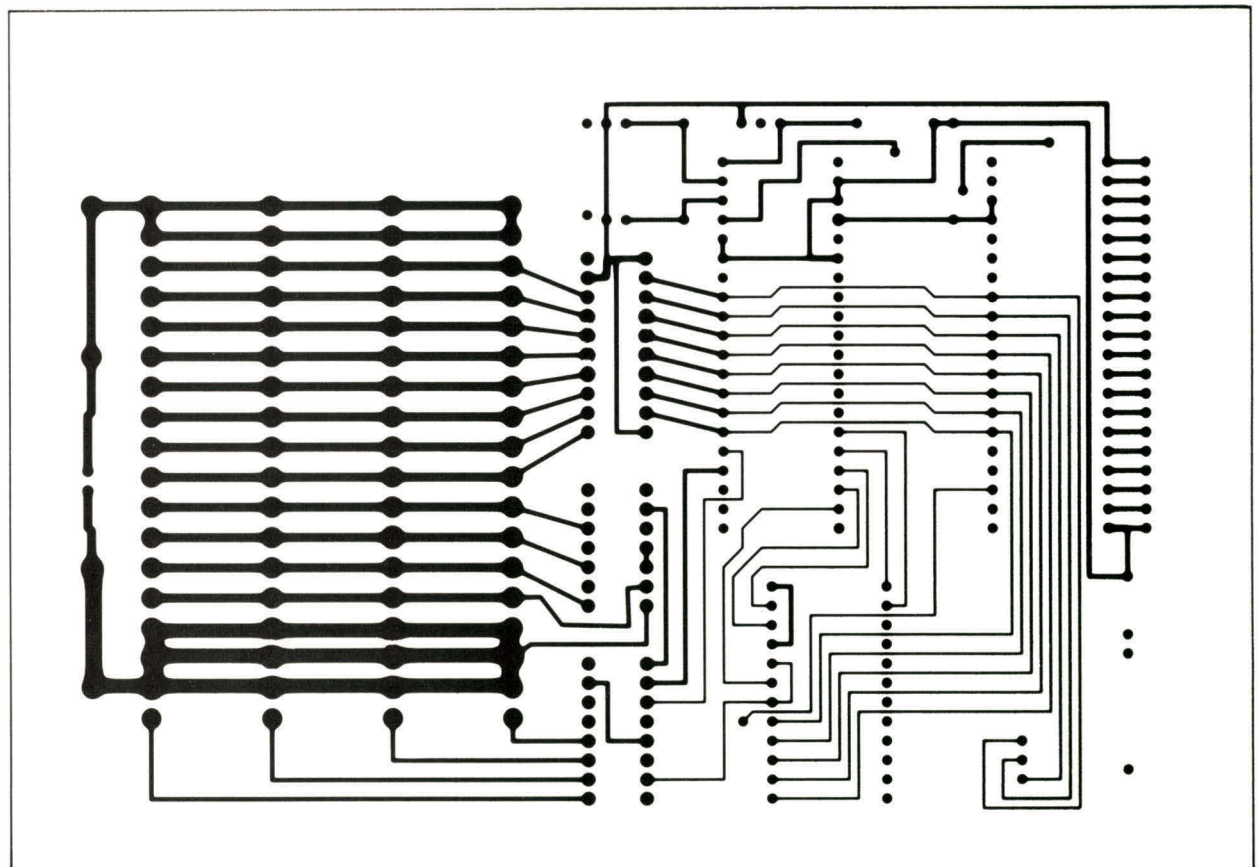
Circuit imprimé vu côté « soudures » de la carte mère.
